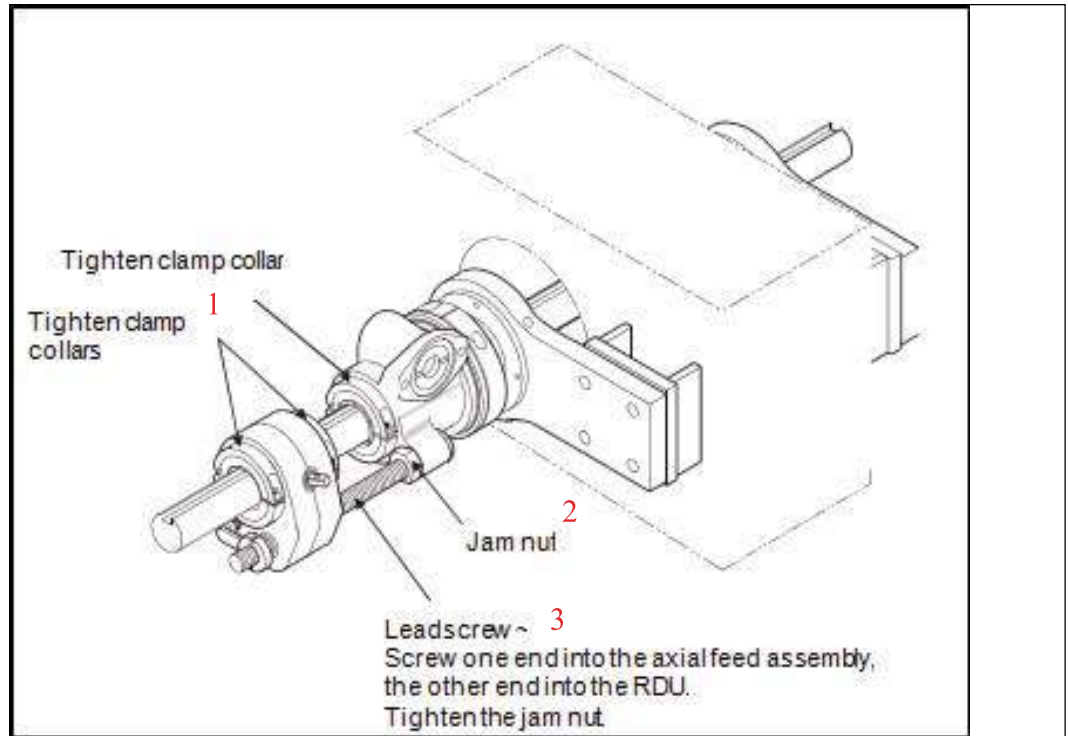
COLLIERS DE SERRAGE SUR L'AFU
